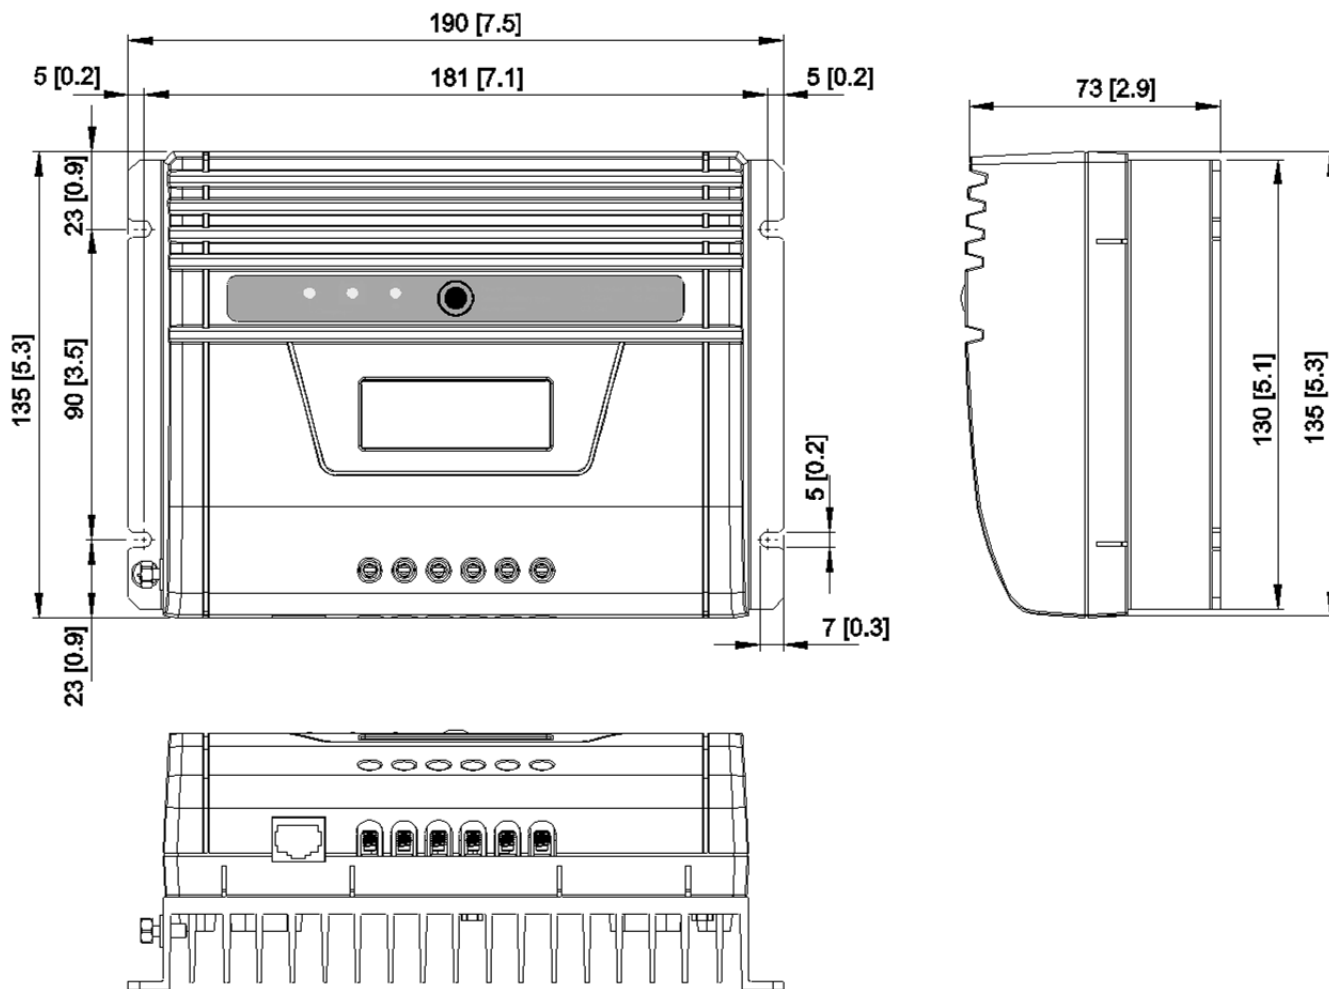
Dimensiones del Solar ChargeMaster en mm [pulgadas]
